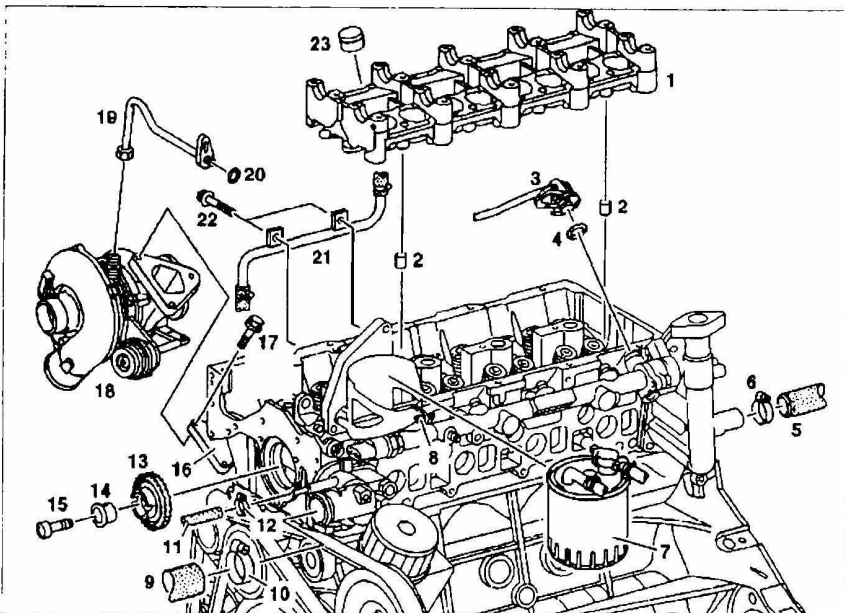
а. Снятие и установка головки блока цилиндров (показано на двигателях 611):
